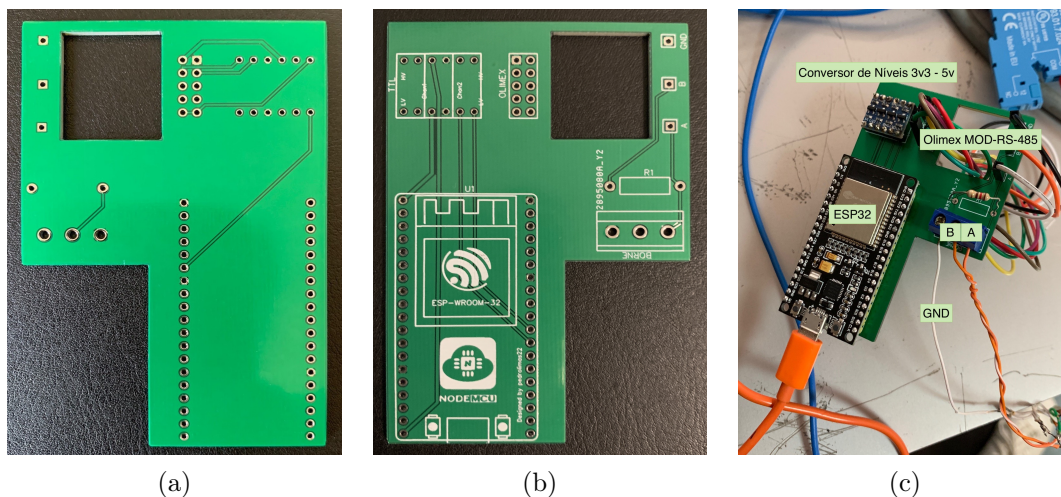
PCB desenvolvida para o projeto: (a) Vista traseira da PCB, (b) Vista frontal da PCB, (c) Vista da PCB com os componentes.
